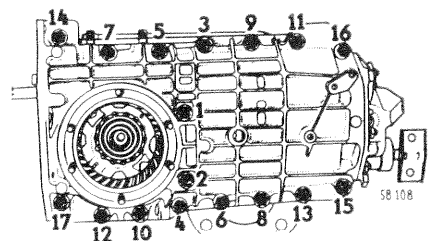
Ordre d'assemblage des boulons de demi-carter
